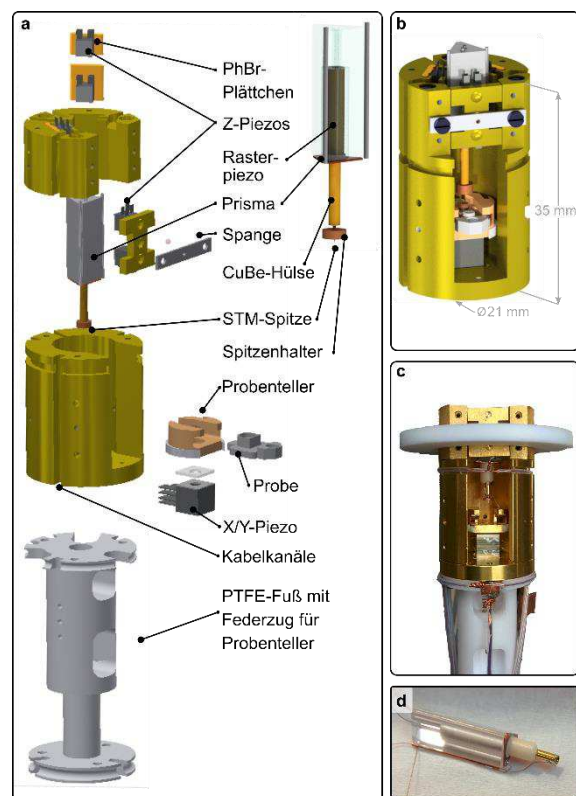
Neuer STM-Kopf. (a) Explosionszeichnung der Hauptbestandteile. (b) Dimensionen des STM-Kopfes. (c) Fotografie des STM-Kopfes, hier mit PTFE-Ring. (d) Prisma mit Rasterpiezo und Spitzenhalterung.
